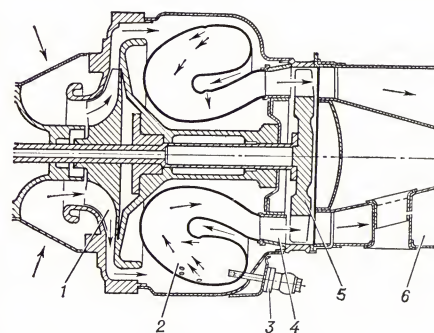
Газотурбинный двигатель: 1 — центробежный компрессор; 2 — камера сгорания; 3 — топливная форсунка; 4 — сопловой аппарат; 5 — рабочее колесо турбины; 6 — выхлопной патрубок.
